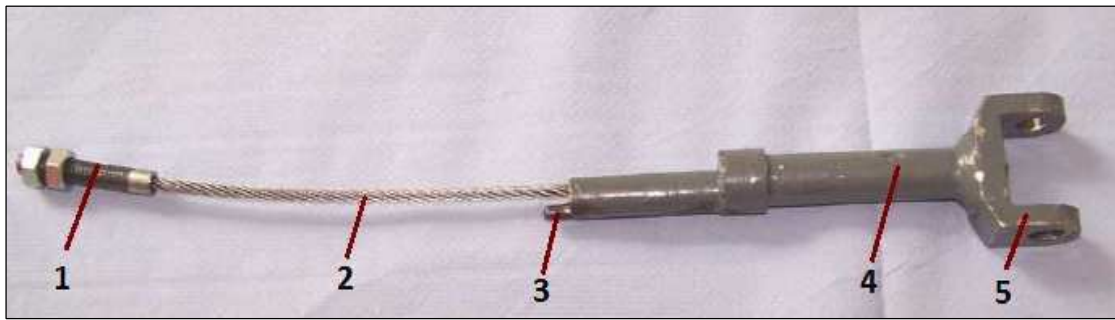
Aufbau der Gelenkstange mit Drahtseil
